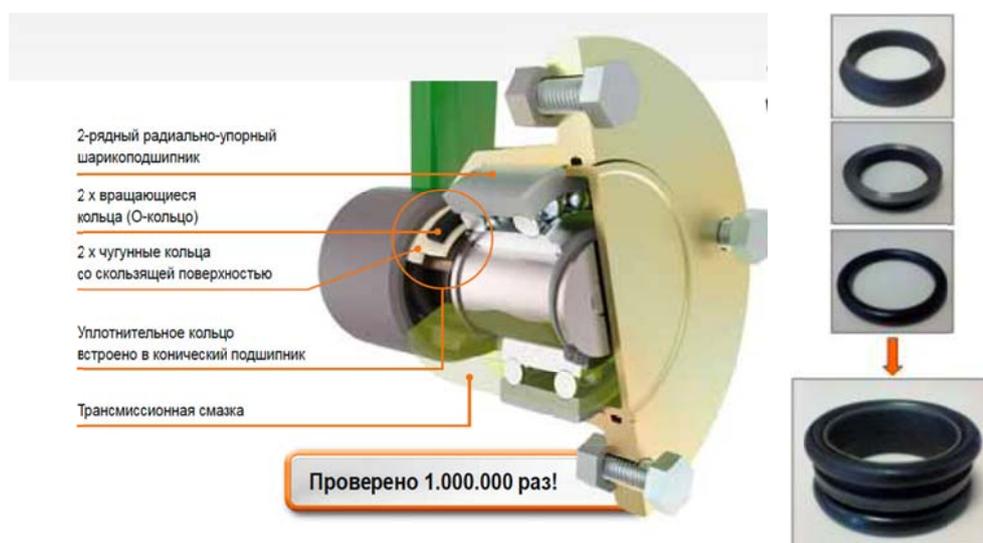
Необслуживаемый подшипниковый узел и прокладки
